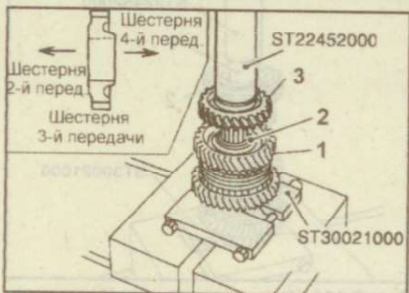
Установка шестерни 2-й передачи (1), подшипника шестерни 2-й передачи (2) и шестерни 3-й передачи (3)
